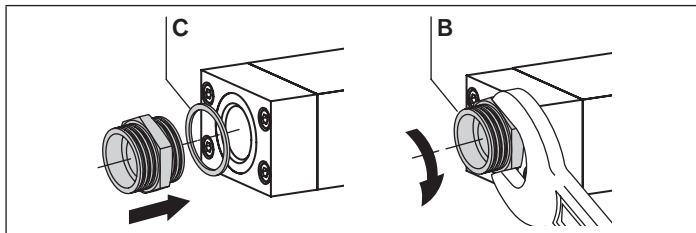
Dichtring anbringen und Anschlussgewinde anschrauben
